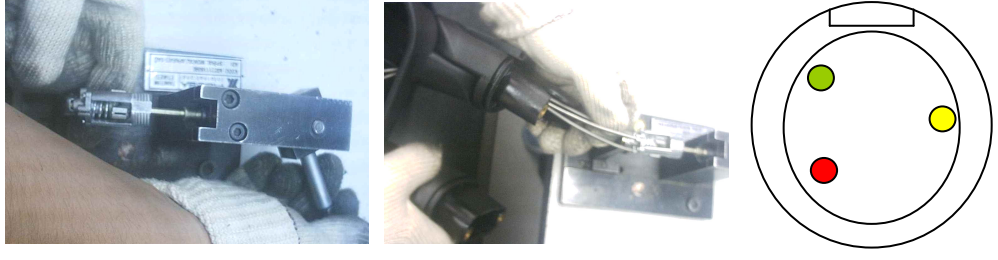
Gövde-kol grubu+spiraller-mekanizma grubu montajı
